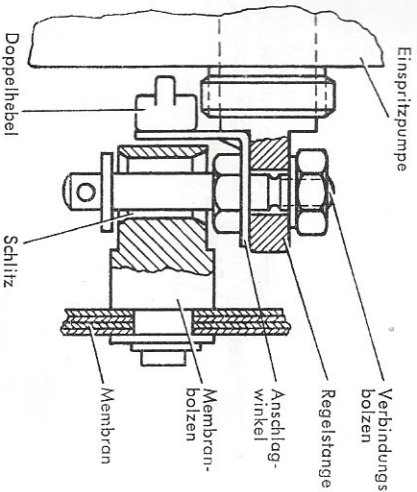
Membranbolzen mit Schlitz, Draufsicht
